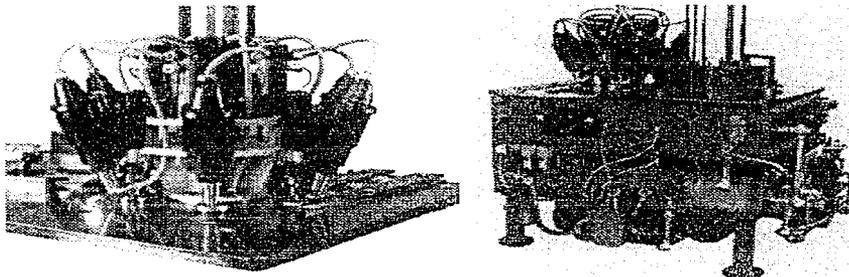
Engomadora rotatoria de seis estaciones, 6 HPS, con pistola electrónica. Cortesía de Preferred Machine Corporation.
